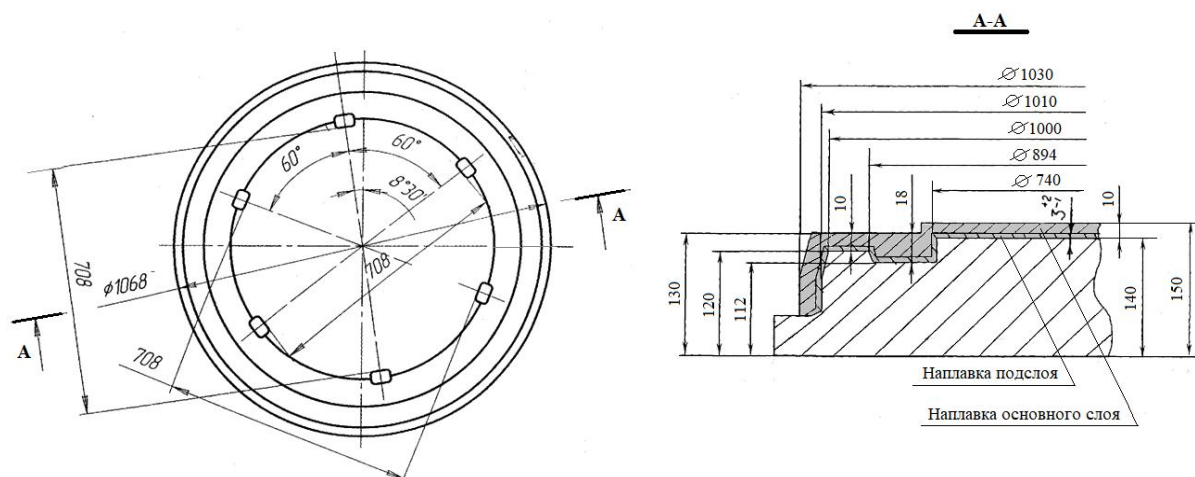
Эскиз внутренней крышки транспортно-упаковочного контейнера ТУК-108/1 (поверхность с наплавкой)
